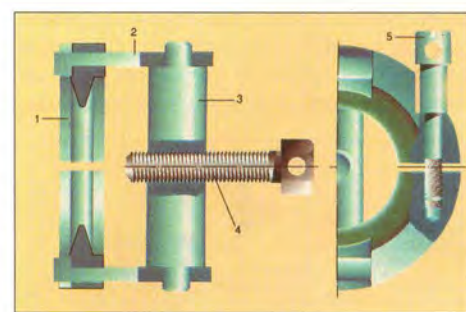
Приспособление в сборе: 1 – шкив генератора; 2 – лапки; 3 – валик; 4 – упорный болт; 5 – стягивающий болт.
